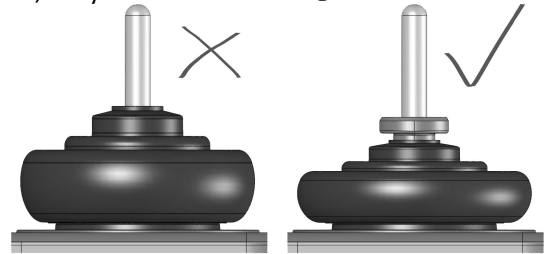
La parte superior de la pieza se asienta por debajo del hombro superior del retenedor del muelle
